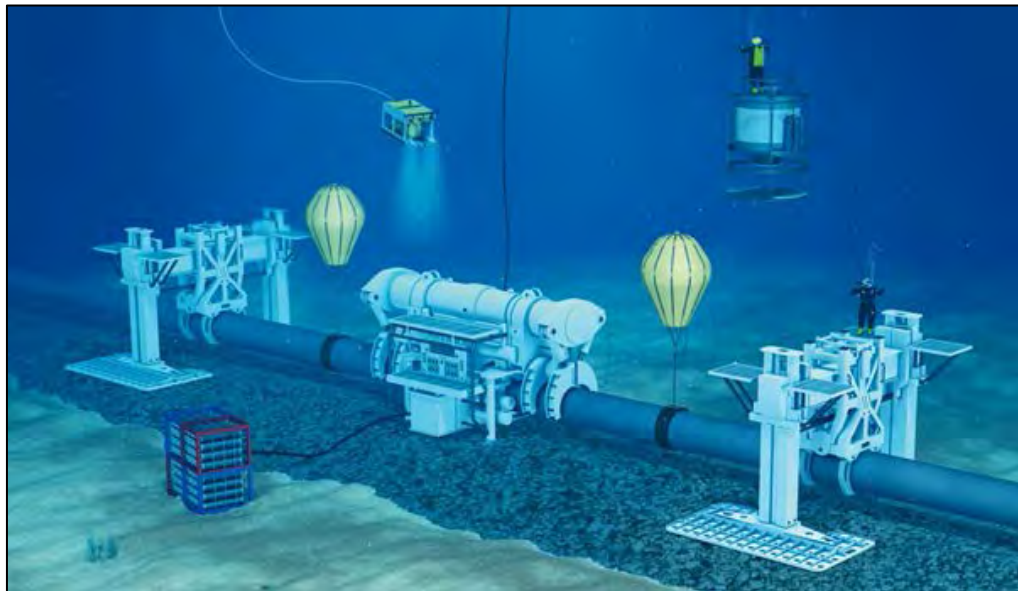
Оборудование для гипербарической сварки.
